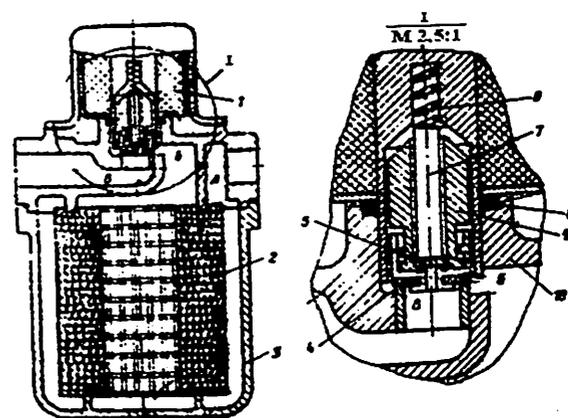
Электромагнитный клапан-фильтр для газа фирмы «Импко карбюрейшн»:
